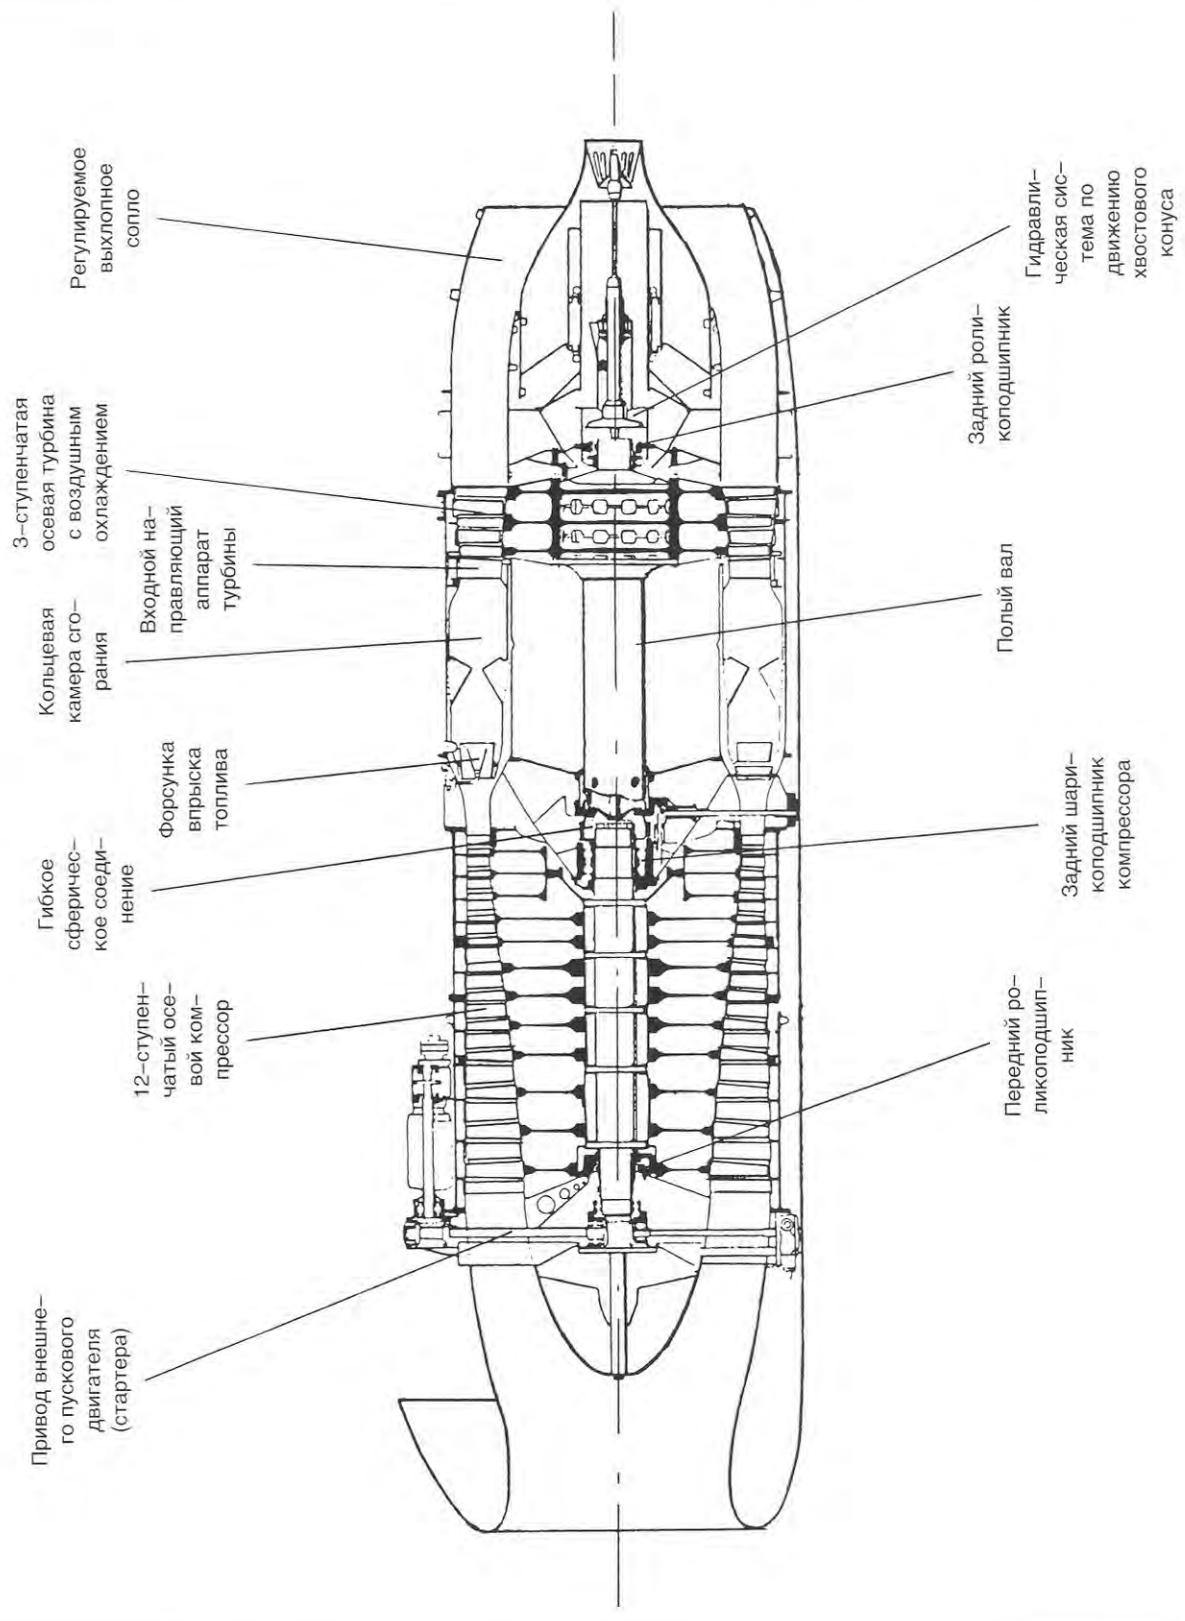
Турбореактивный двигатель БМВ 109-018
